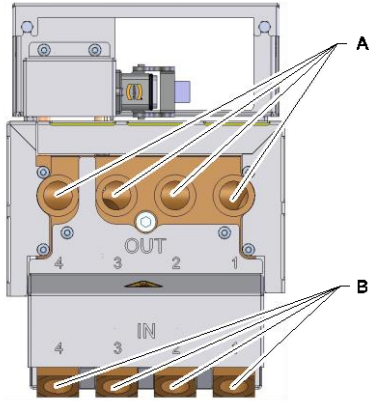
Racorduri la acest mod de construcție: Structura aparatului/structura aparatului separat
